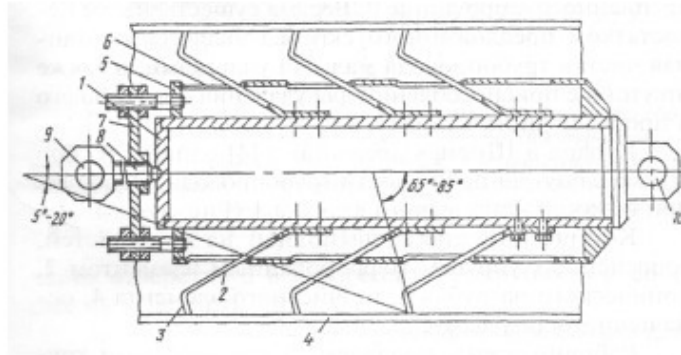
Устройство для поэтапной очистки внутренней поверхности трубопровода, где 1 – корпус; 2 – пружинящие металлические пластины; 3 – скребки; 4 – очищаемый трубопровод; 5 – кожух; 6 – окна; 7 – опорный диск; 8 – винт; 9, 10 – пружины.
